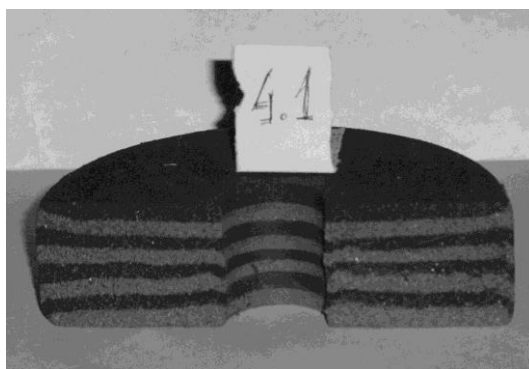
Сечение заготовки абразивного круга умеренной высоты после прессования из двойной заготовки с переворотом
